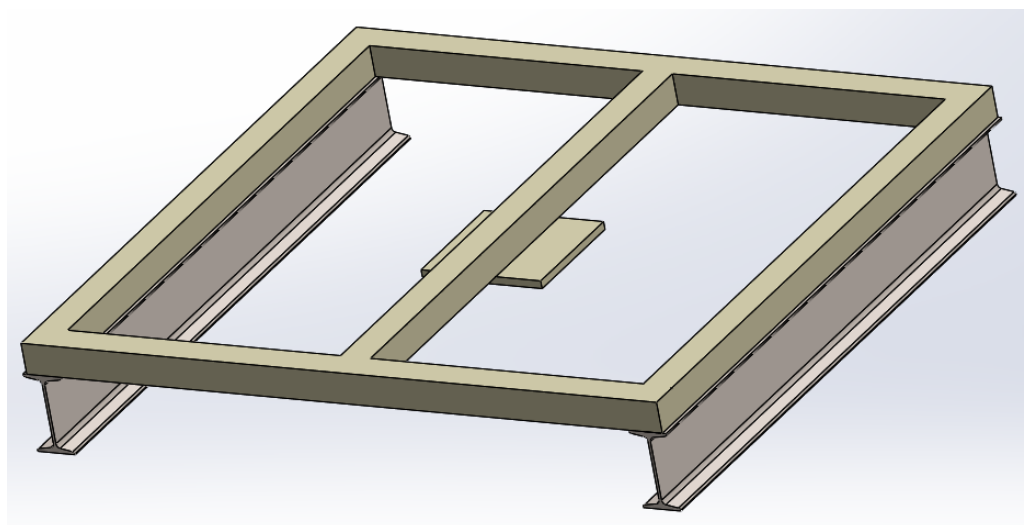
Návrh základní kovové konstrukce vibračního třídiče
